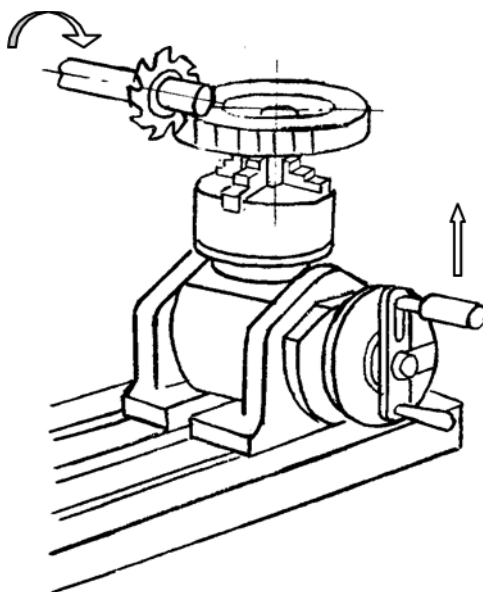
Фрезерование зубьев цилиндрического колеса
